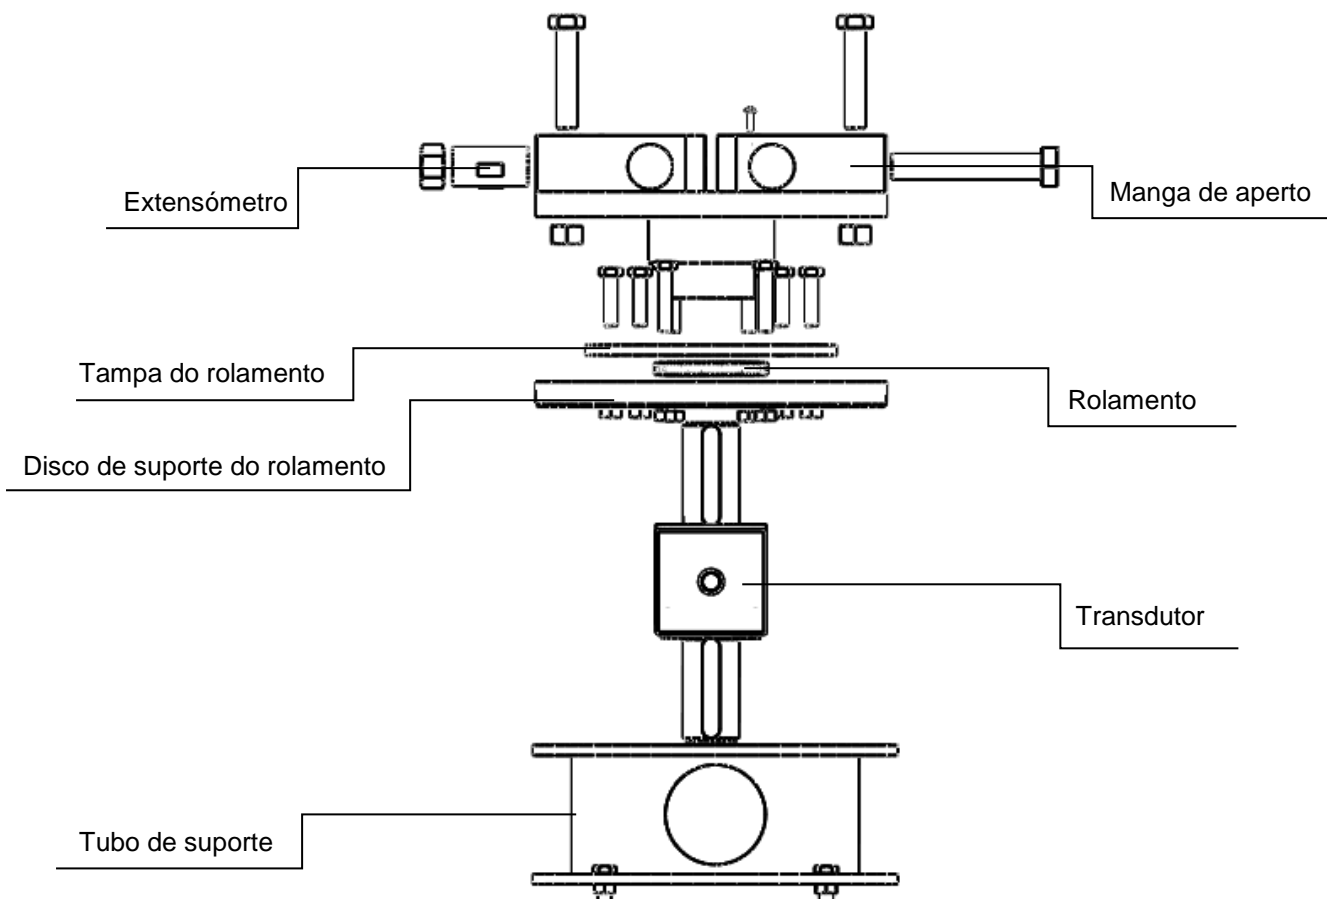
Vista explodida dos componentes centrais do mecanismo.
